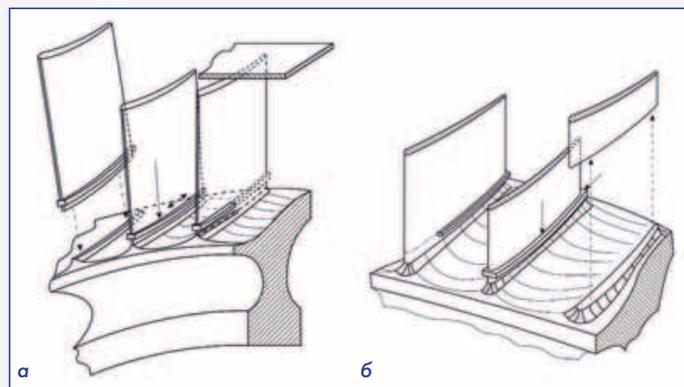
Изготовление моноколес с помощью сварки трением:
